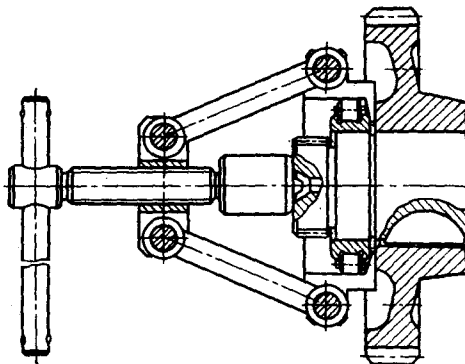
Снятие внутреннего кольца переднего подшипника промежуточного вала
